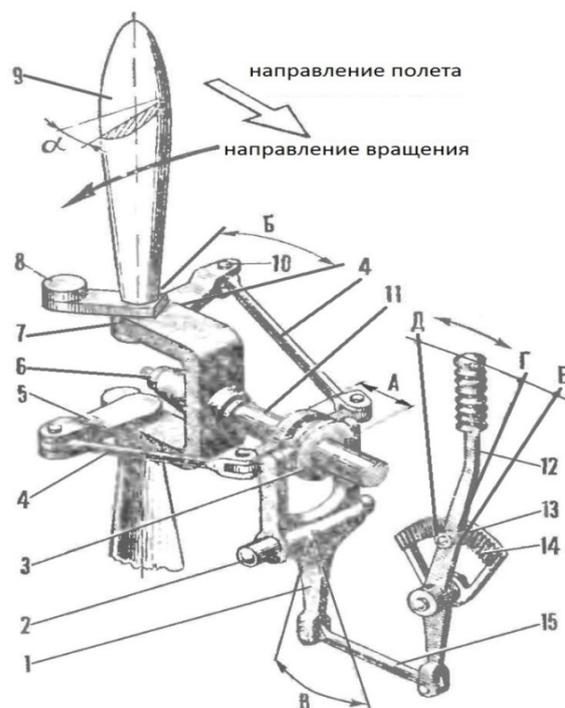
Схема ВИШ [4]: 1 – промежуточная качалка; 2 – ось; 3 – скользящая муфта; 4 – тяга управления; 5 – рычаг лопасти; 6 – гайка крепления втулки; 7 – втулка винта; 8 – противовес; 9 – лопасть; 10 – шарнир тяги; 11 – приводной вал; 12 – рычаг управления изменением шага винта в кабине водителя; 13 – фиксатор рычага управления; 14 – зубчатый сектор; 15 – тяга. А – ход муфты; Б – ход рычагов лопасти; В – ход промежуточной качалки; Г – ручка в положении малого шага; Д – ручка в положении большого шага; Е – ручка в положении реверса
